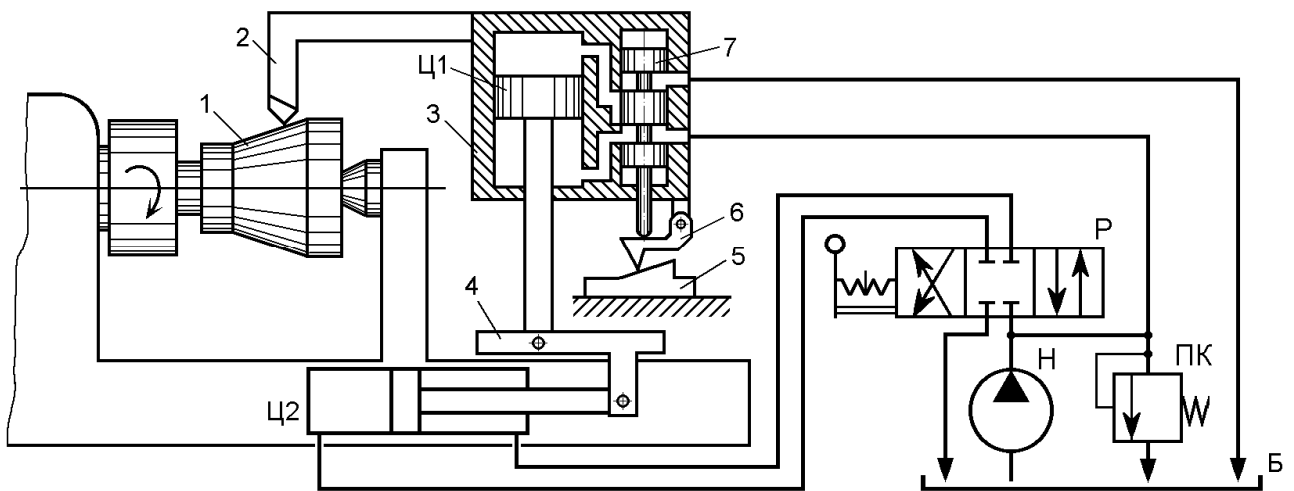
Схема токарного станка с гидрокопировальным устройством
